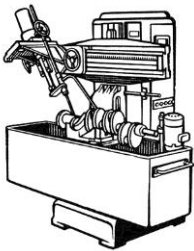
Верстат для електроерозійної обробки колінчастих валів
